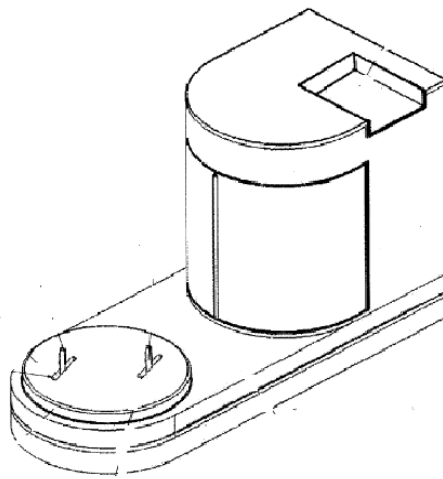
Схема пристрою для упаковки в полімерну плівку, вид в аксинометрії
